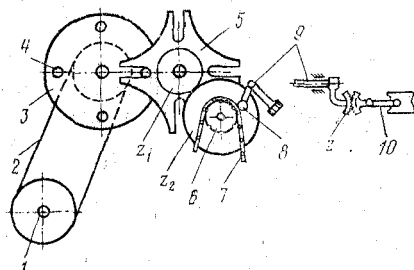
Схема двухуточного прибора станка СТБ2-216
